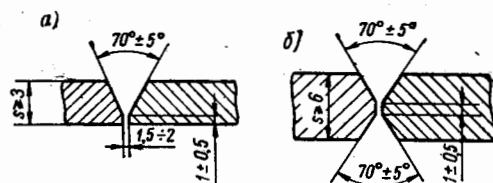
Конструктивные элементы подготовки кромок листовой стали марок Х16Н6, свариваемой ручной электродуговой сваркой: а — V-образная разделка кромок; б — X-образная разделка кромок
